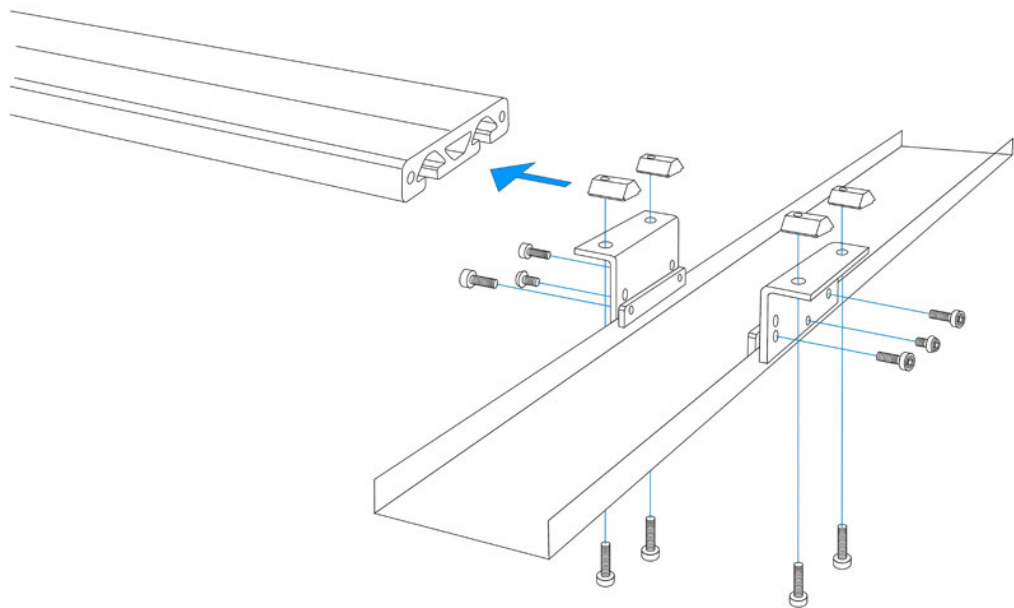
Fixation de chenal suspendue sur la barre profilée
